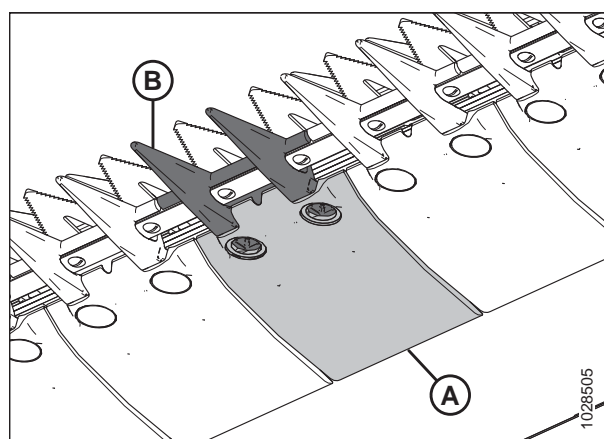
Центральный противорезущий палец и износная пластина
